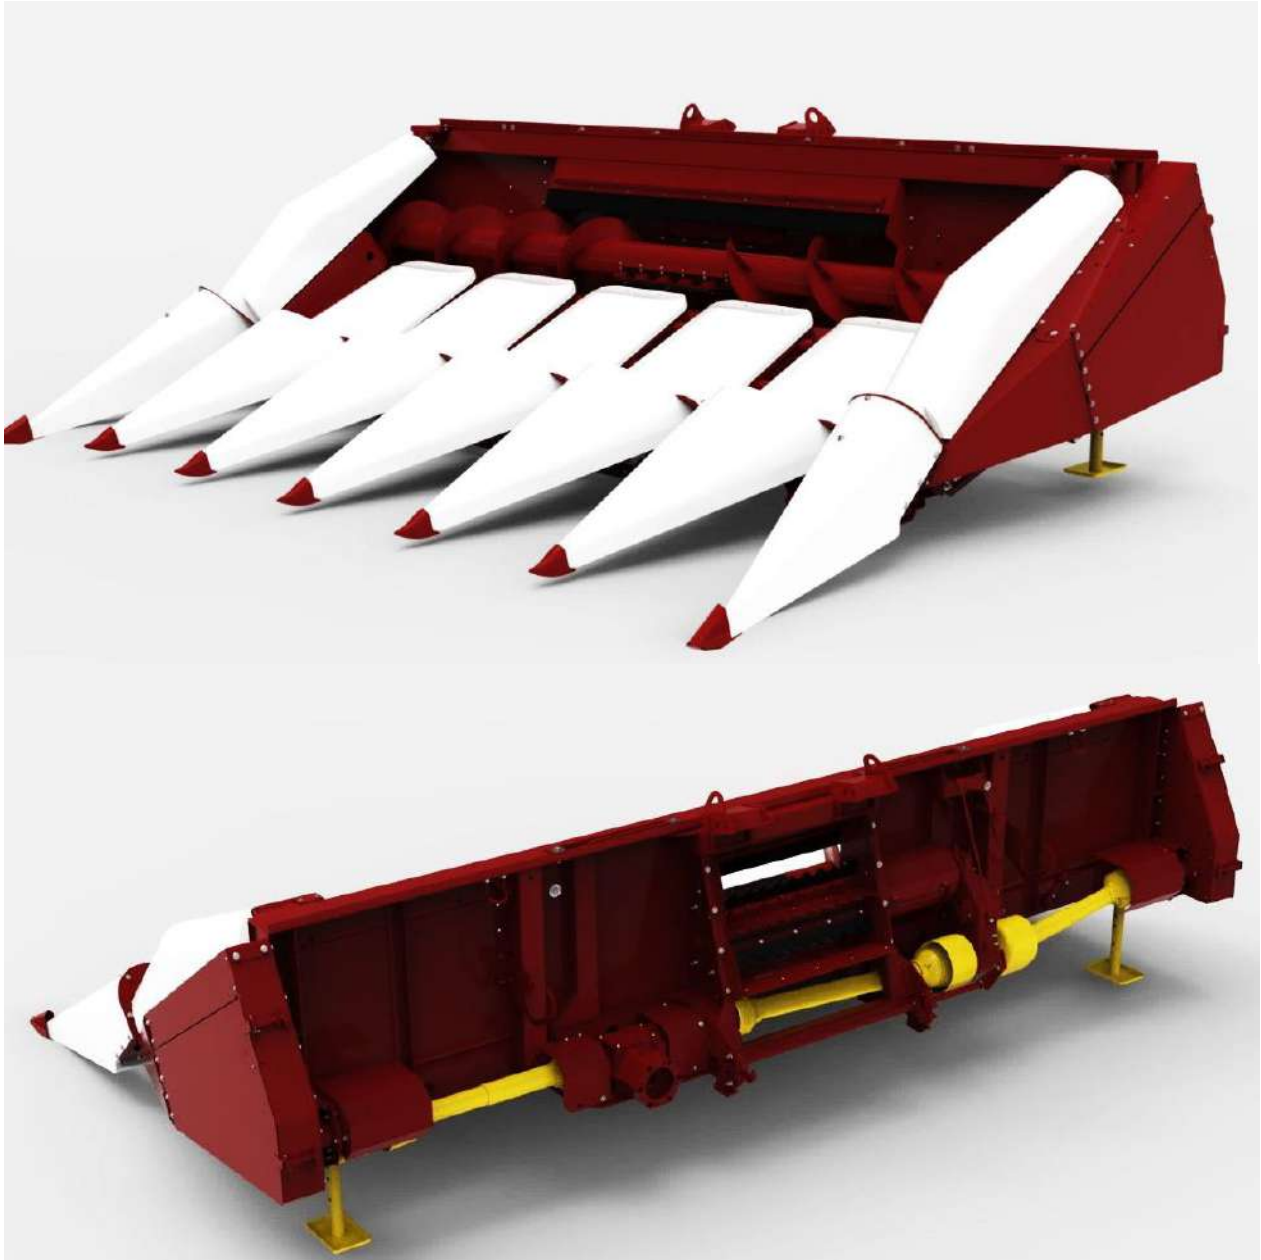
Общий вид 6-рядной жатки для уборки корняжа.
